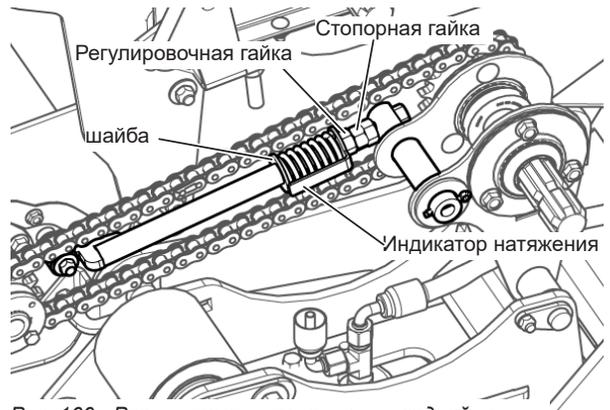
Регулировка натяжения приводной цепи центрального транспортера
